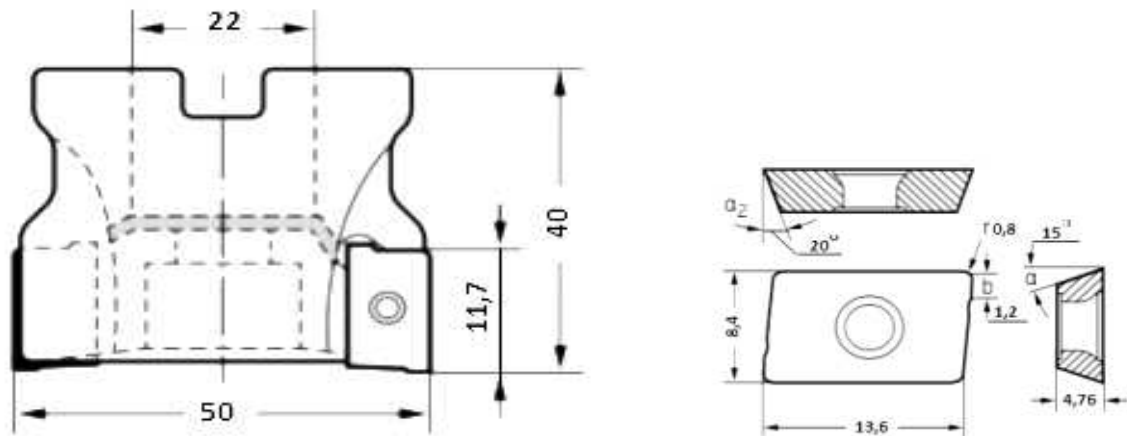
фреза F4042.B.050.Z06.11, пластина ADKT1204PER-F56
